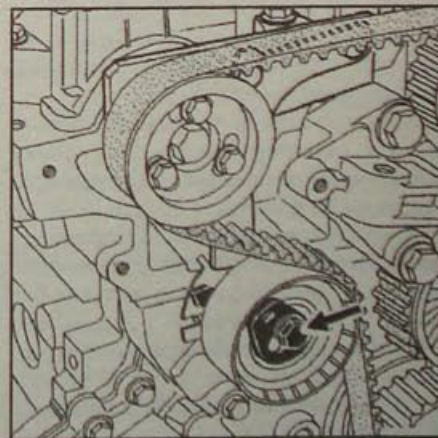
Расположение болта крепления натяжного ролика ремня привода газораспределительного механизма
